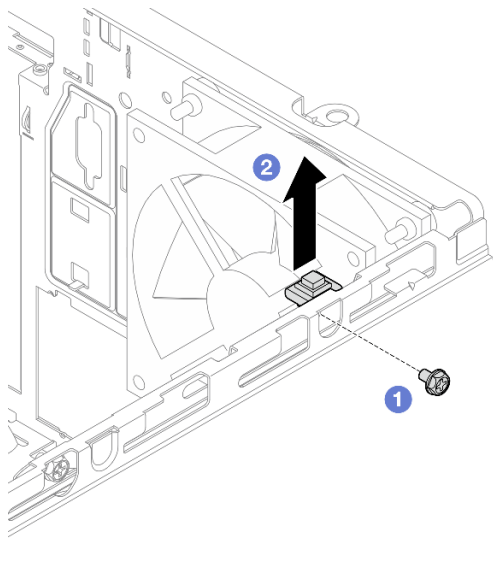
Entfernen des Schalters gegen unbefugten Zugriff
